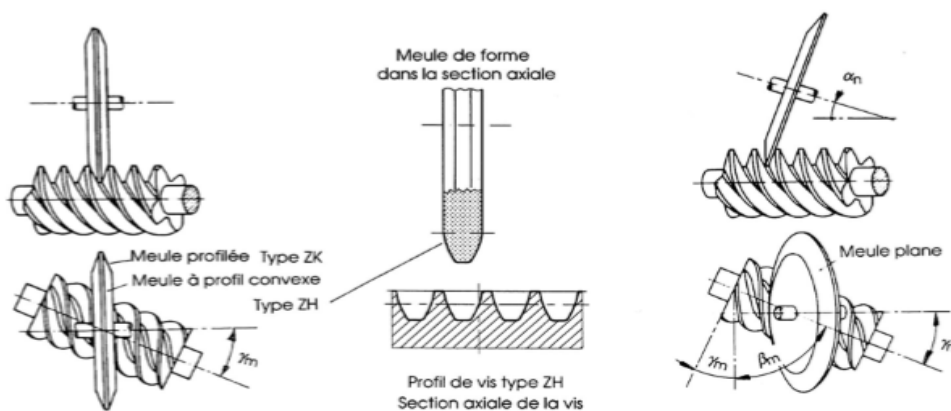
Définition et fabrication des flancs de la vis : vis de types ZK, ZH et ZI.
